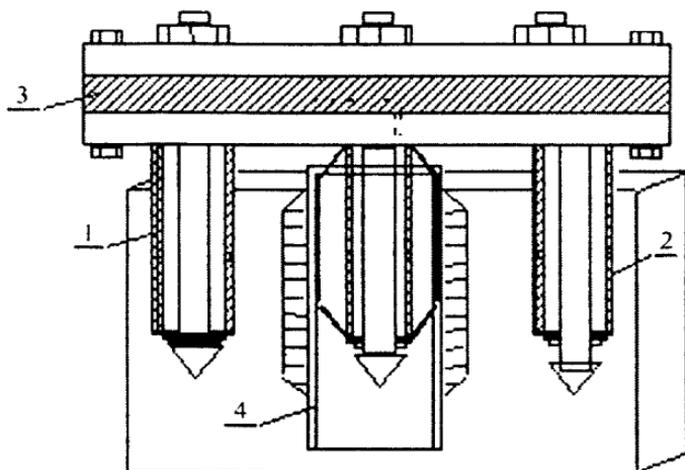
Групповое захватное устройство для извлечения шпуль с нитью из коробки:
